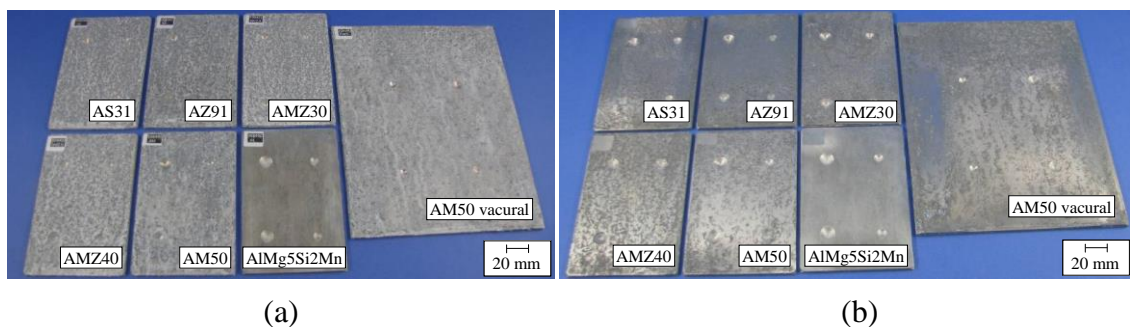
Druckgussplatten nach 48h Salzsprühnebeltest (a) und nach Entfernung der Korrosionsprodukte (b)
